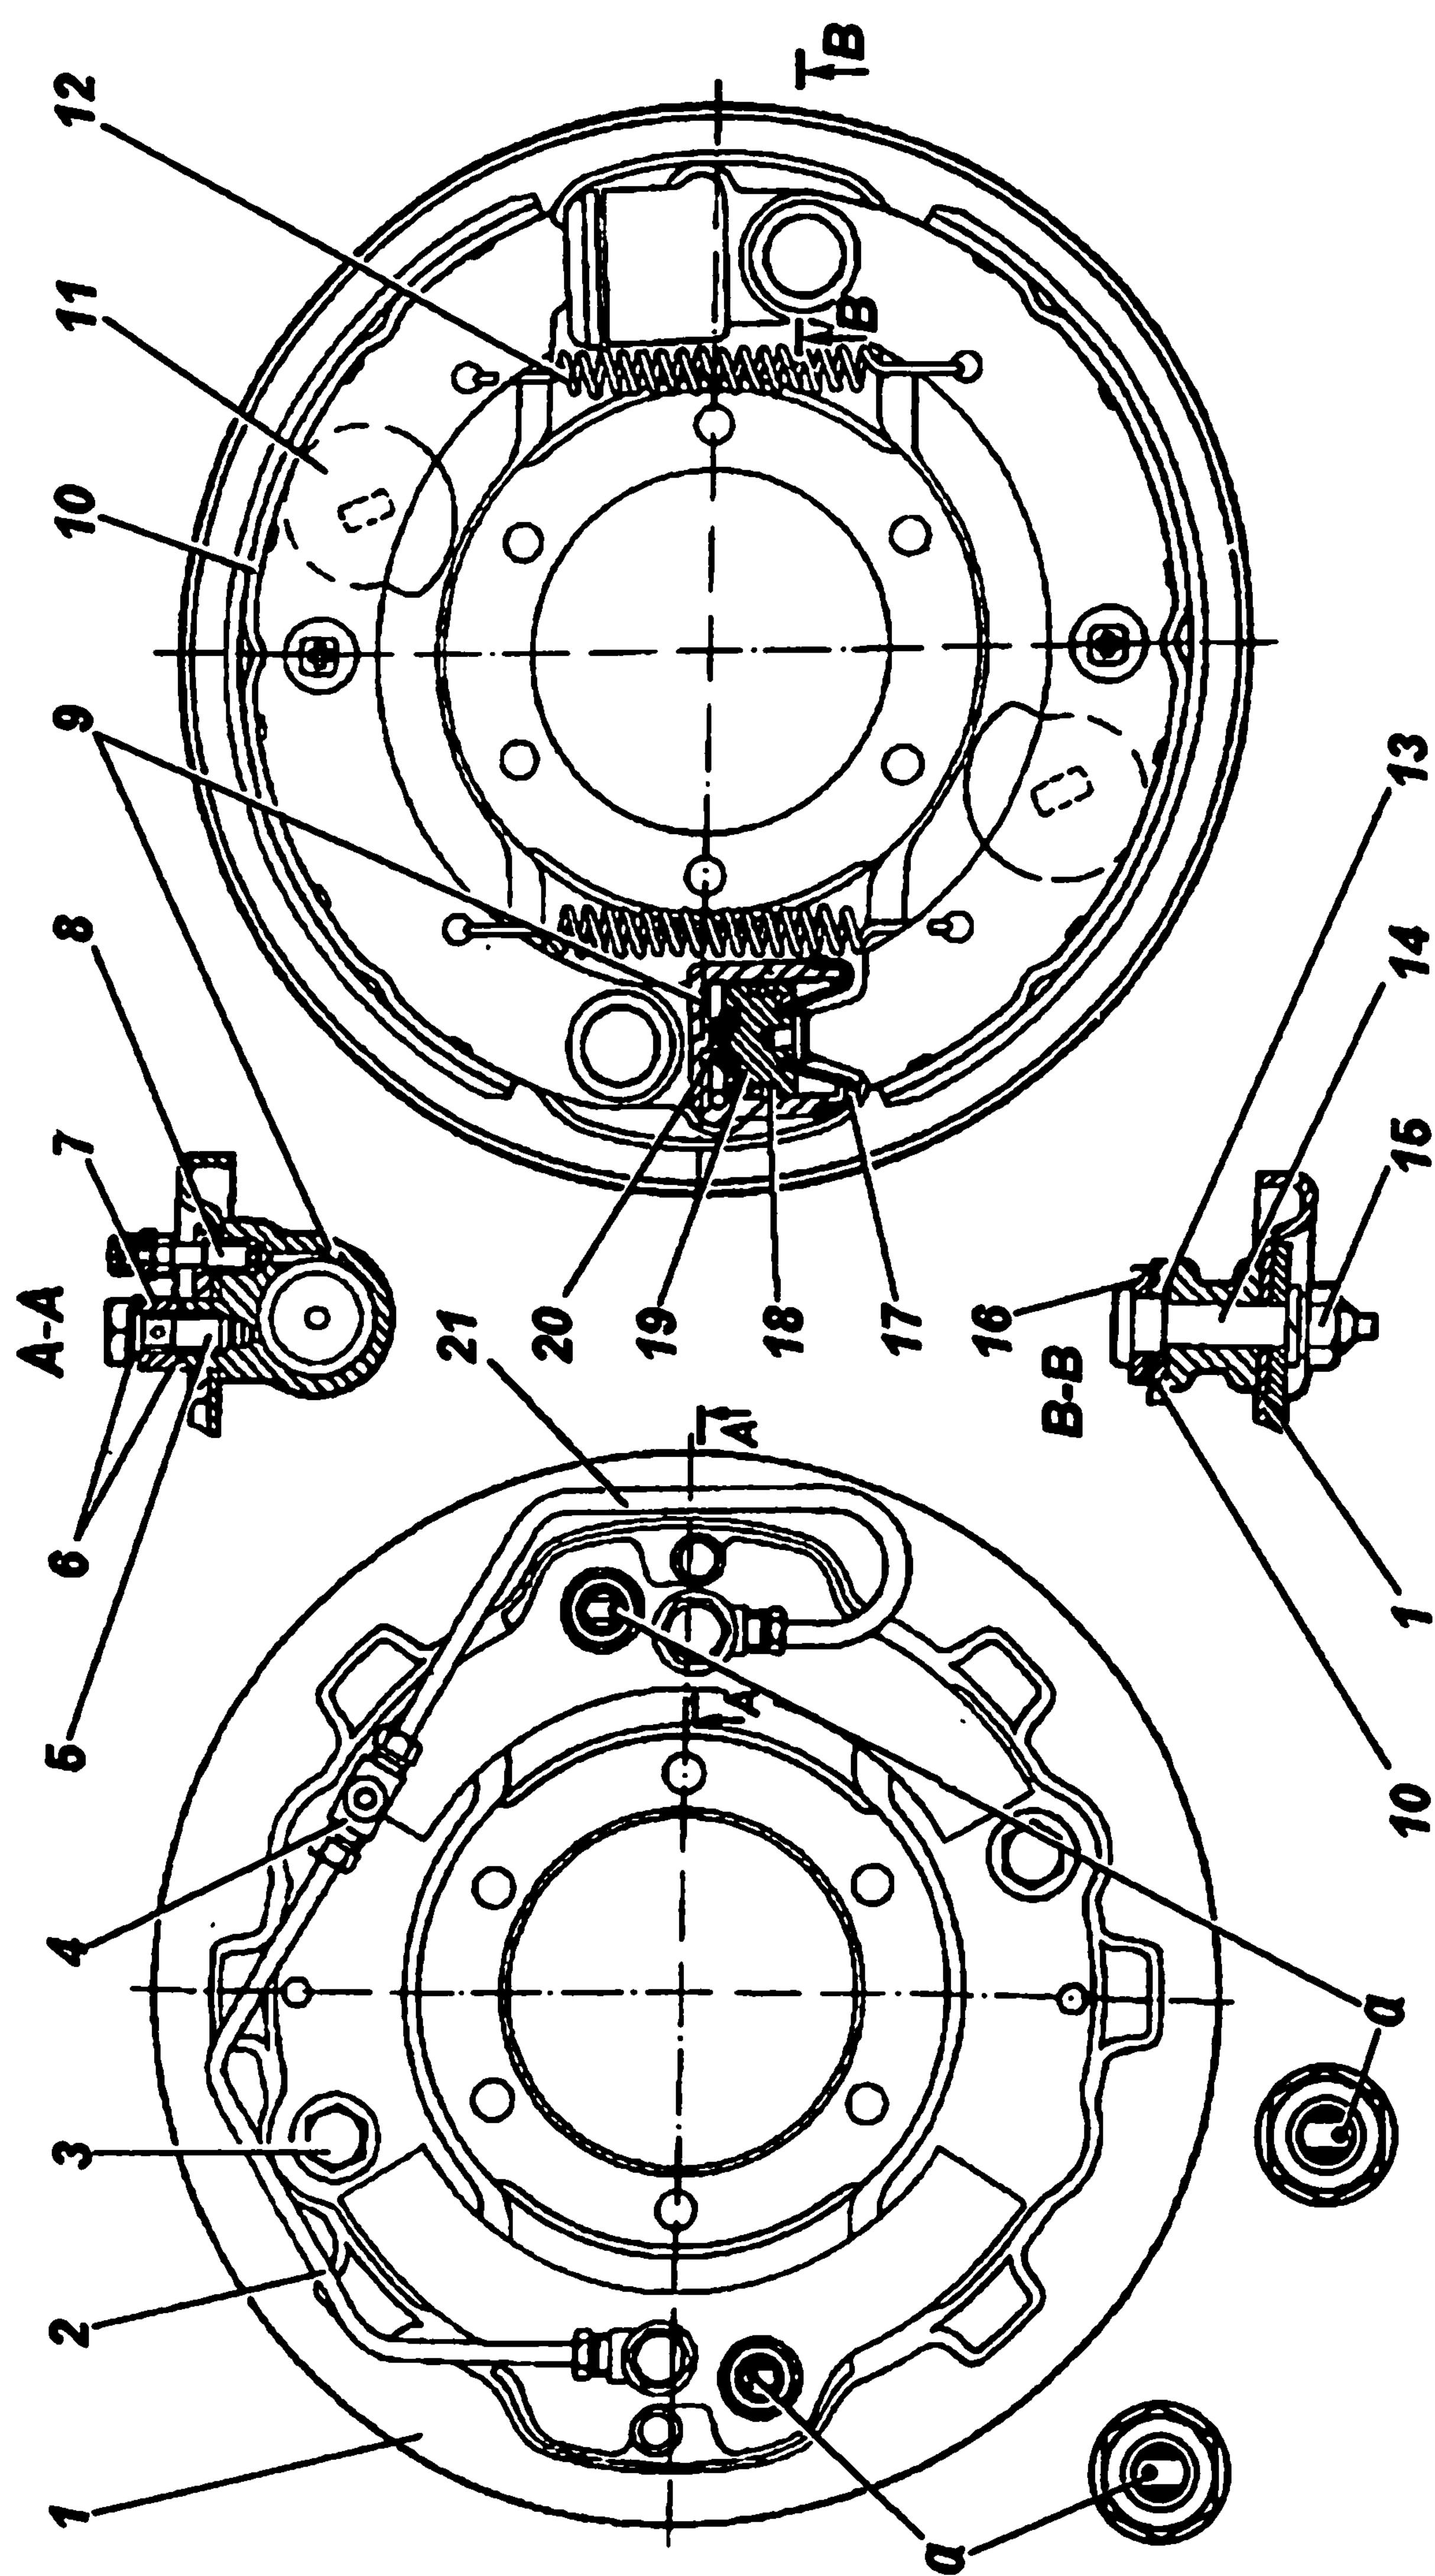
Тормоз переднего колеса автомобиля УАЗ-3151:
